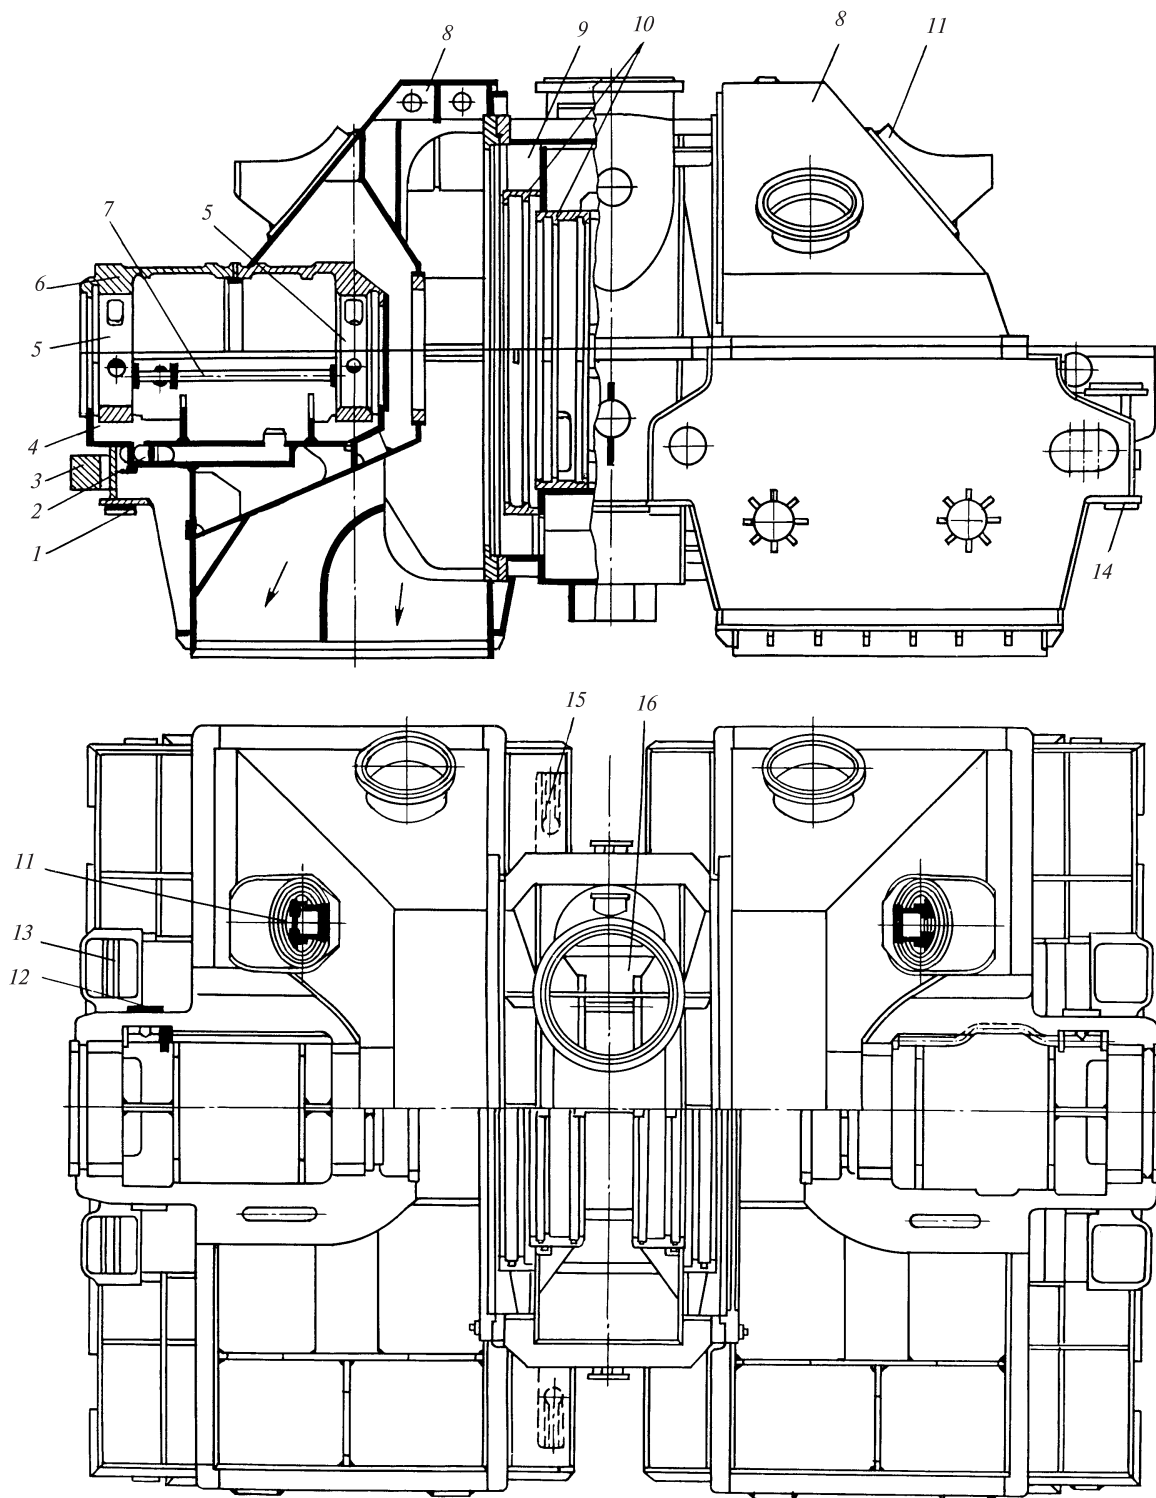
Конструкция одностенного корпуса ЦНД
